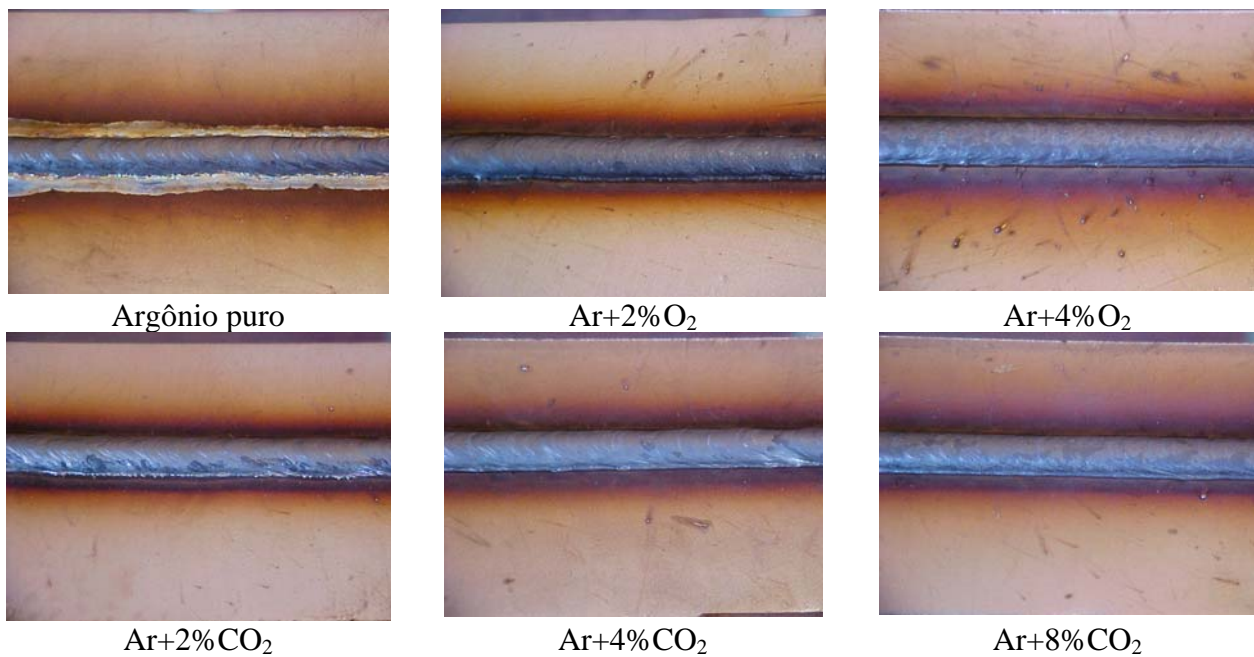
Aspecto do cordão de solda para o arame eletrodo ER430LNb.
